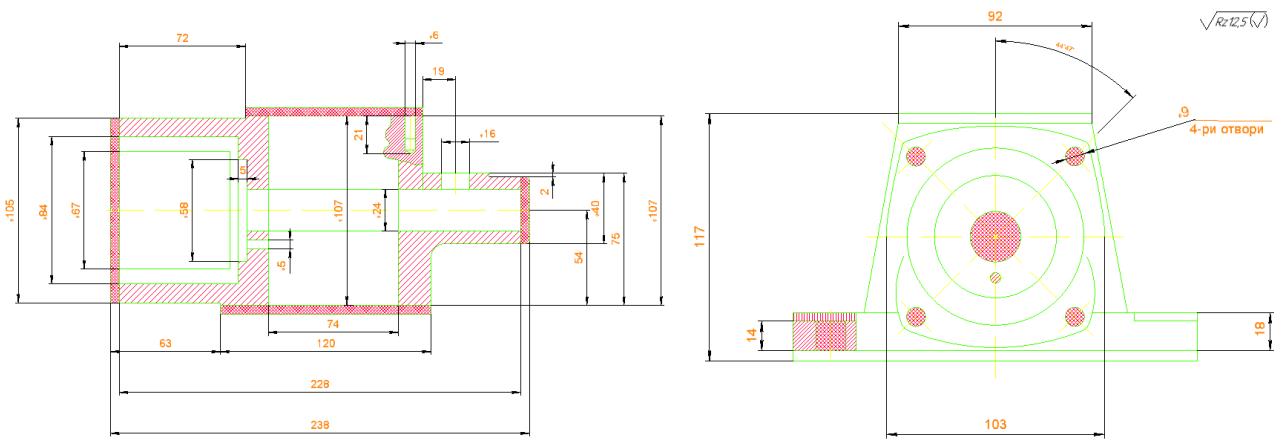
Креслення моделі деталі корпус КС-4372.104.10.003
